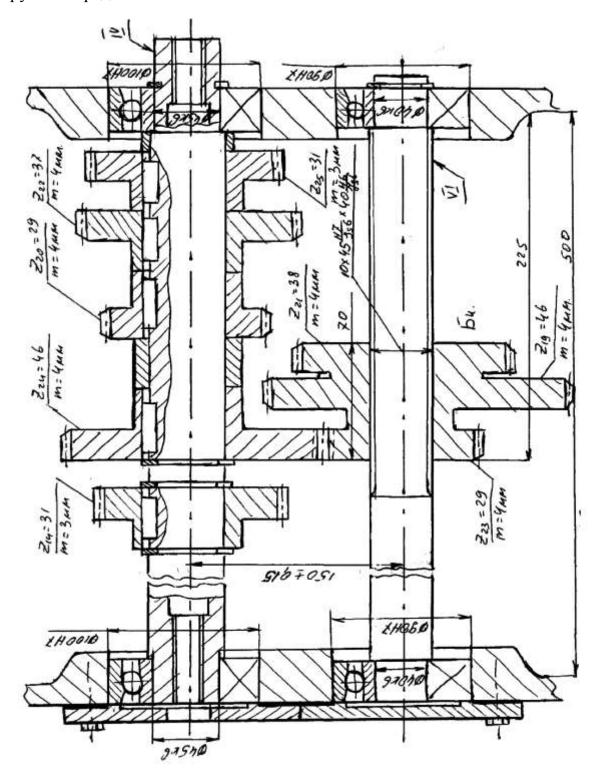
Сборочный чертеж наиболее нагруженной группы передач
